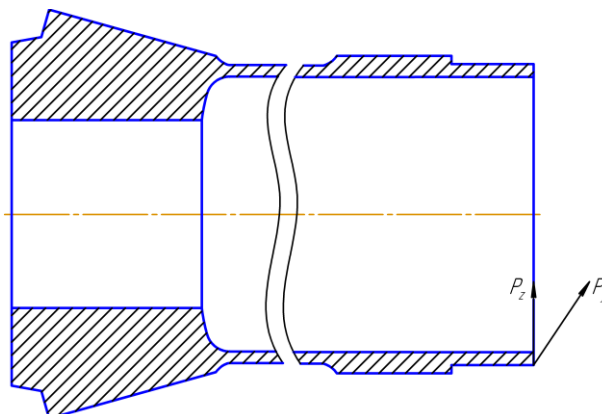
Эскиз заготовки с приложенными силами P_z и P_y
